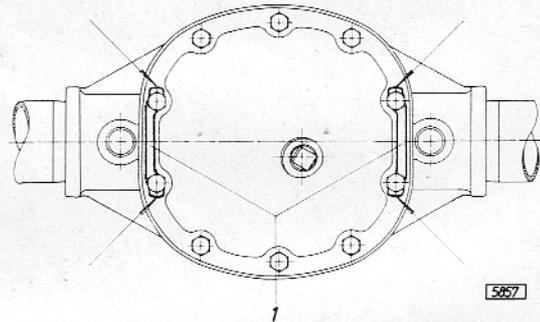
Befestigung Hinterachsgehäusedeckel
